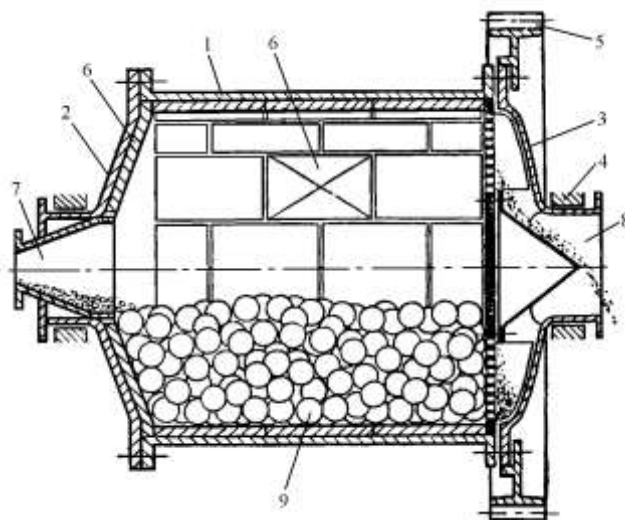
Барабанная мельница: 1 – корпус; 2, 3 – крышки; 4 – подшипник; 5 – зубчатый венец; 6 – плита футеровки; 7 – загрузочная цапфа; 8 – разгрузочная цапфа; 9 – мелющие тела
